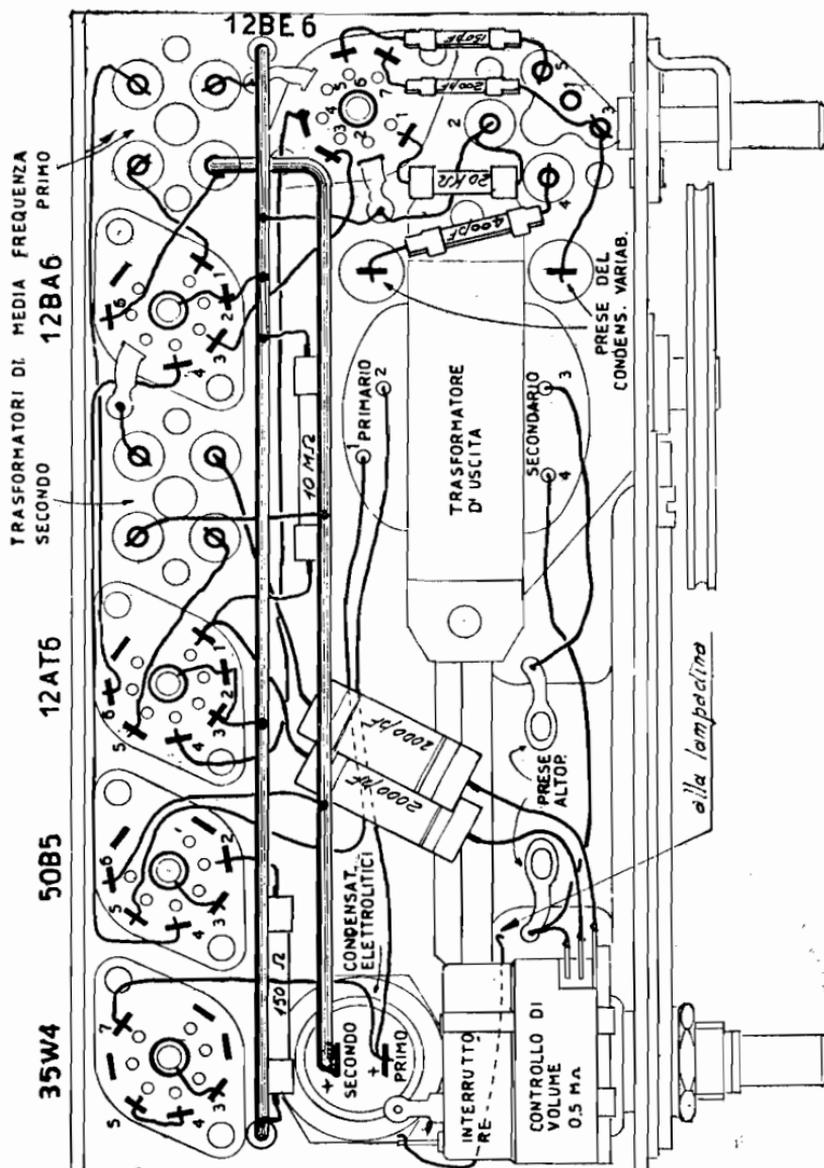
Prima fase del montaggio sotto il telaio.
